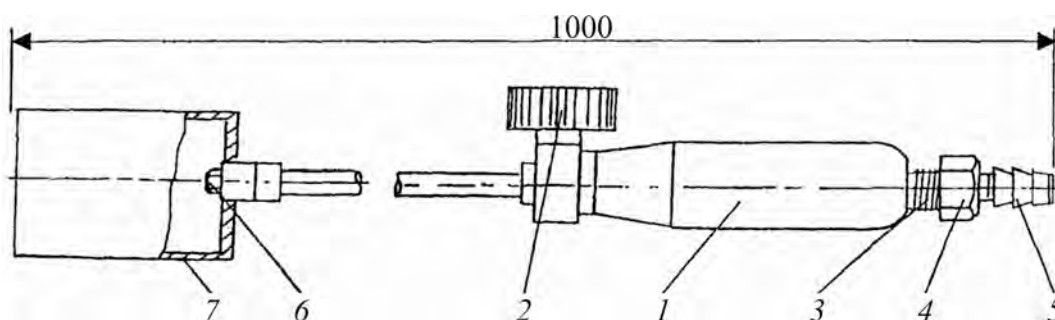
Горелка газоздушная ГВ-1-02П: 1 — ствол с рукояткой; 2 — регулировочный вентиль; 3 — штуцер; 4 — накидная гайка; 5 — ниппель; 6 — инжектор (сопло); 7 — стакан
